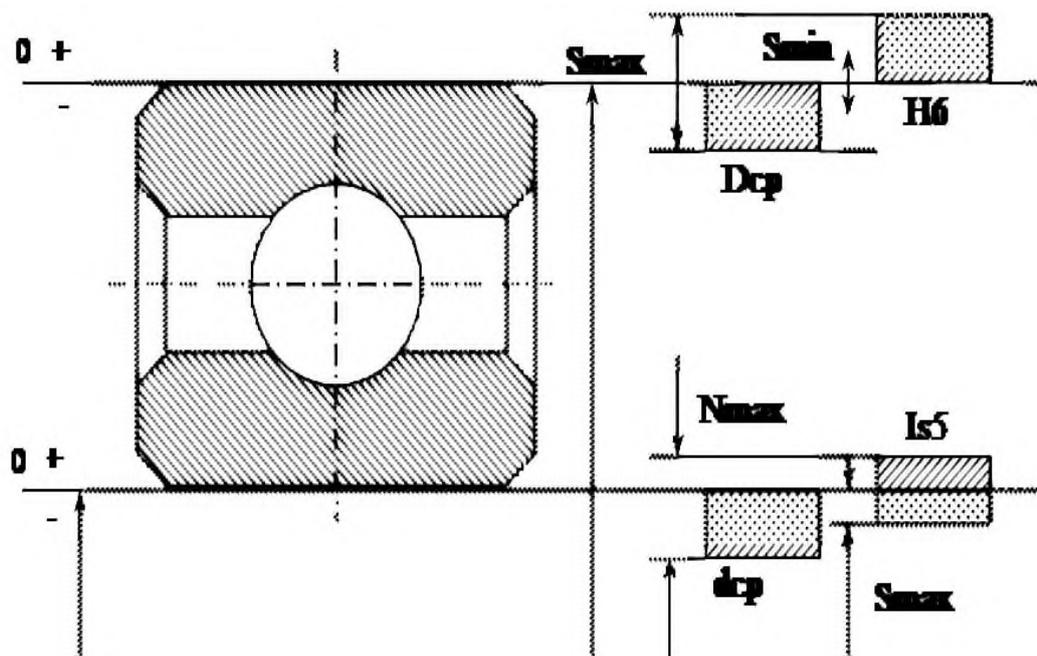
Расположения полей допусков колец подшипника и сопрягаемого с ними вала и отверстия в корпусах
